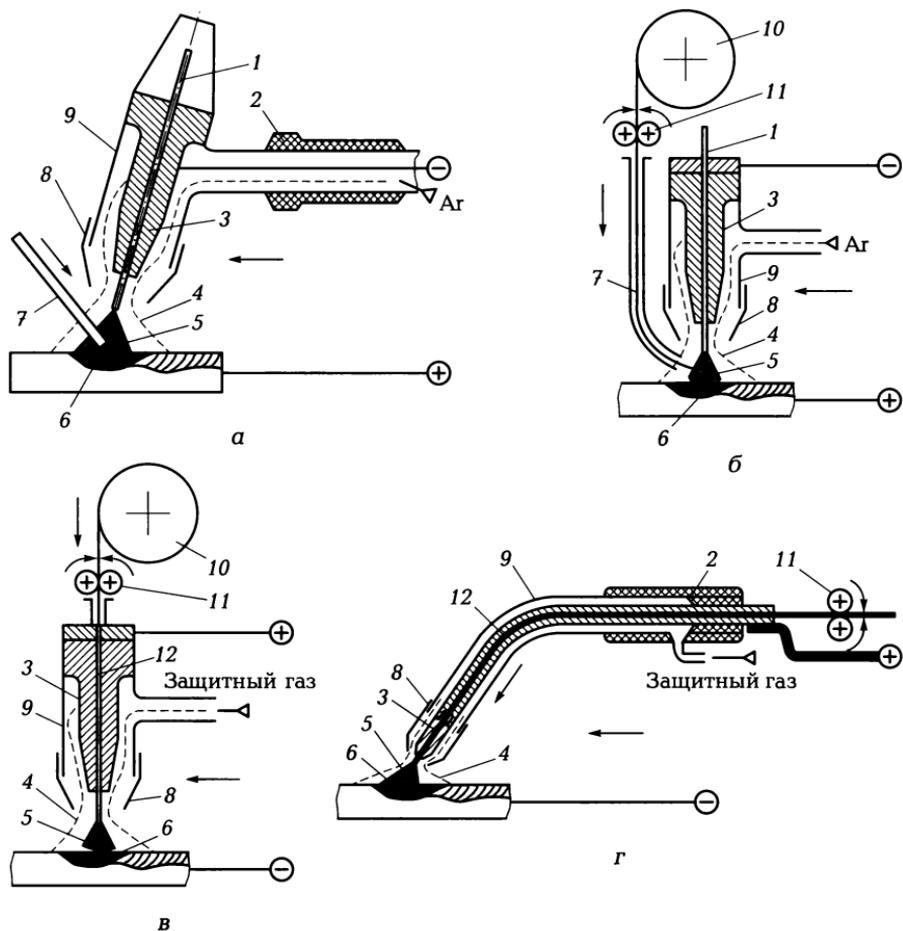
Разновидности аргодуговой сварки:
